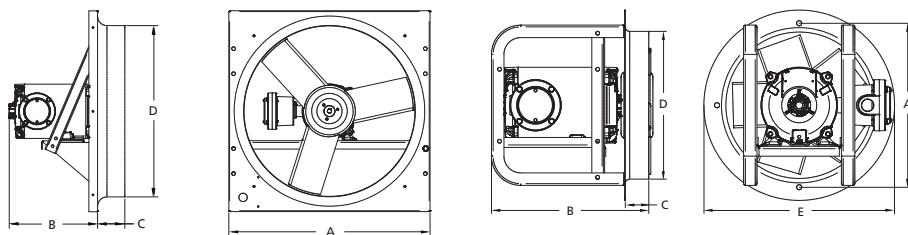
Dimensiones del Ventilador de Panel Figura 2 — Dimensiones del Ventilador de Anillo
